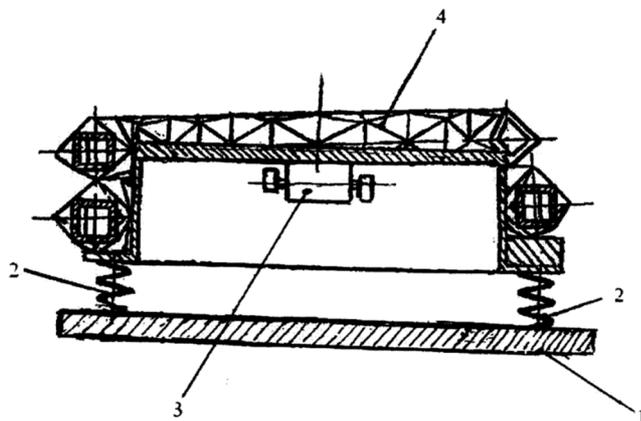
Устройство малогабаритное для приготовления лакокрасочной продукции
